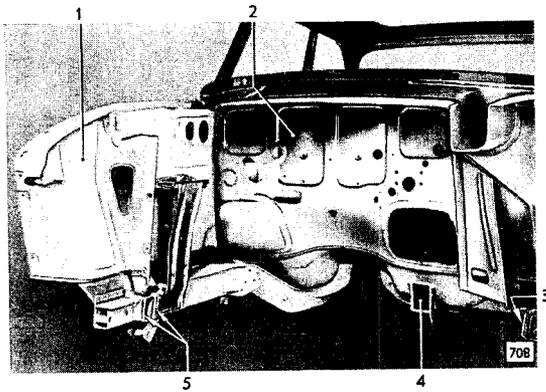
Vorderrahmenlängsträger mit Seitenstrebe, Querträger, Radeinbau und Luftleitblechen abgenommen
